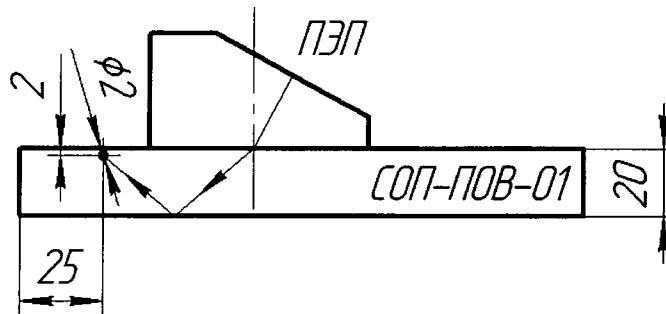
Установка акустического блока на поверхность СОП-ПОВ-01 для получения сигнала от бокового сверления диаметром 2 мм.
